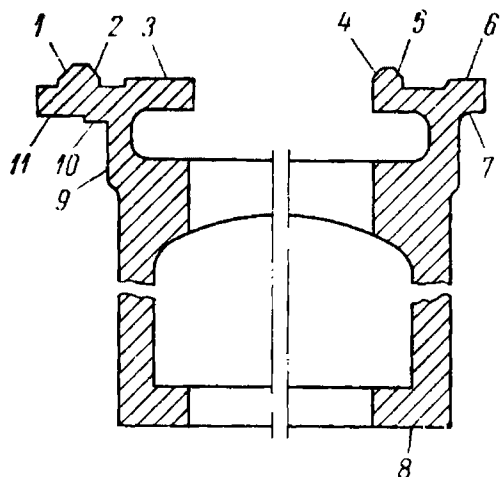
Профиль направляющих станины токарно-винторезного станка модели 1К62
